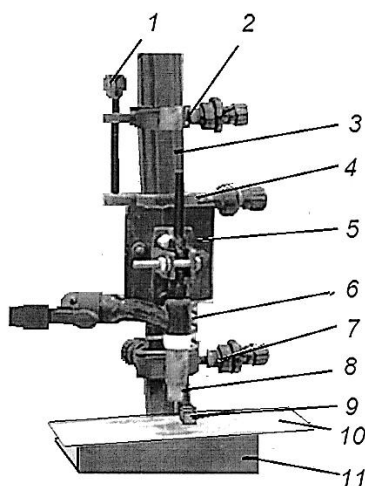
Штатив с горелкой для аргонодуговой сварки
